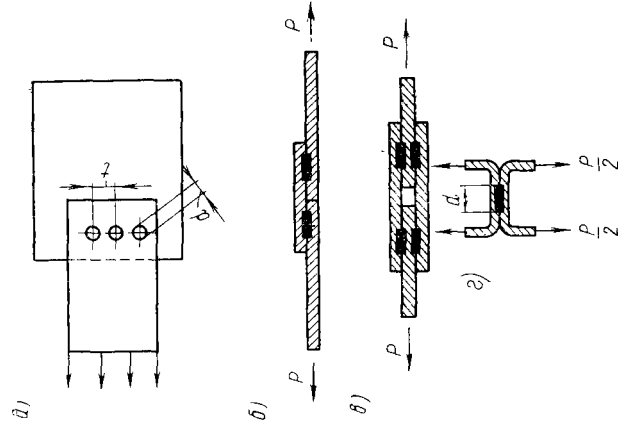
Точечное соединение, работающее на срез и отрыв:
